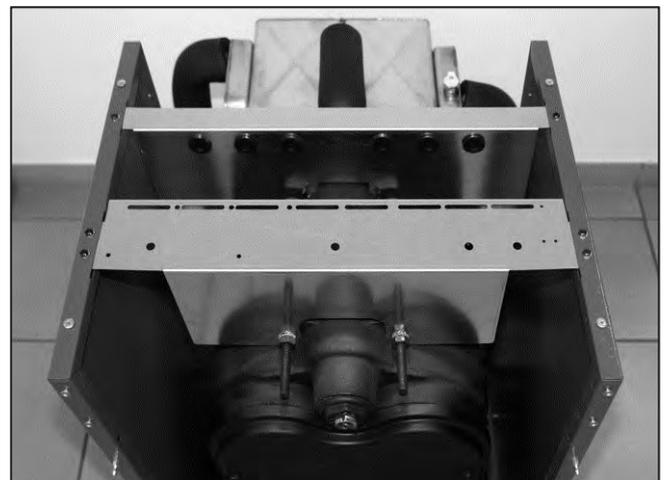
Seitenbleche mit Blechschrauben unter Verwendung der Zahnscheiben fest anziehen.
